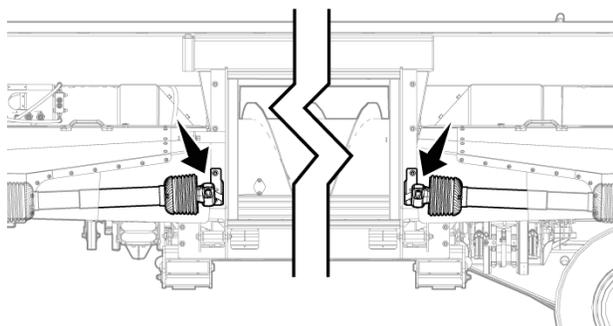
Posizioni di stoccaggio dell'albero motore
